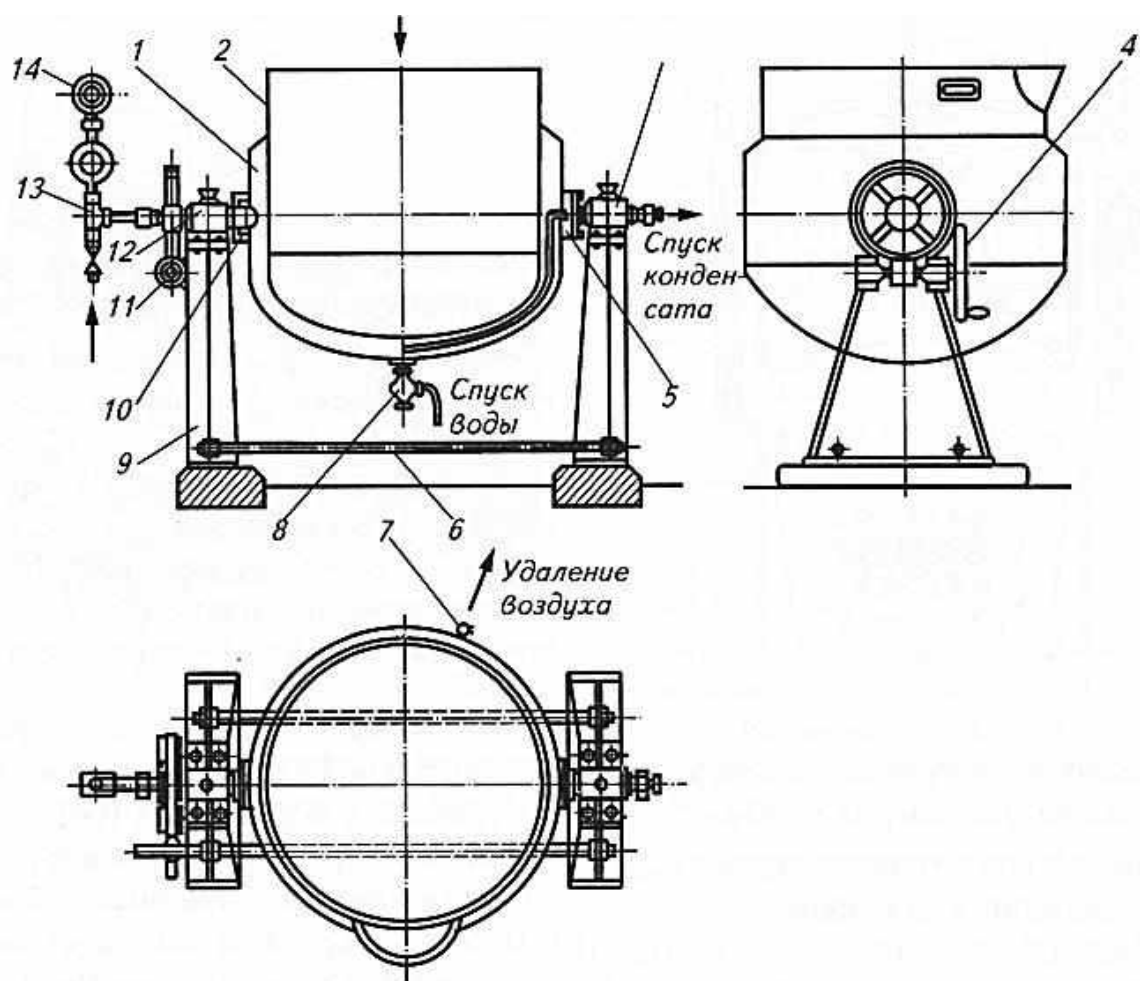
Котел варочный опрокидывающийся К7-ФВ2А
